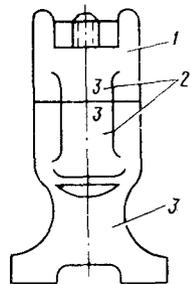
Обозначение спаренности корпуса и крышки подшипника валов распределительных:
